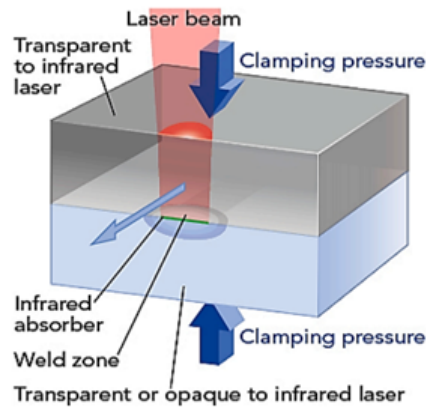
Ilustração do processo de soldadura por transmissão de laser [1].
